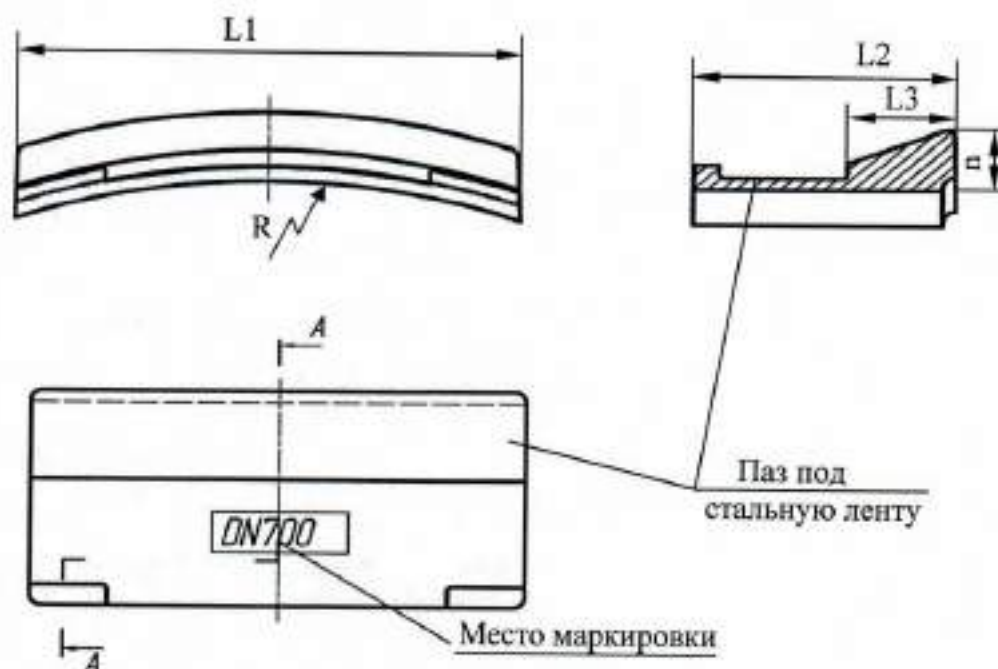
Стопорный элемент из ВЧШГ для соединения «RJS».
